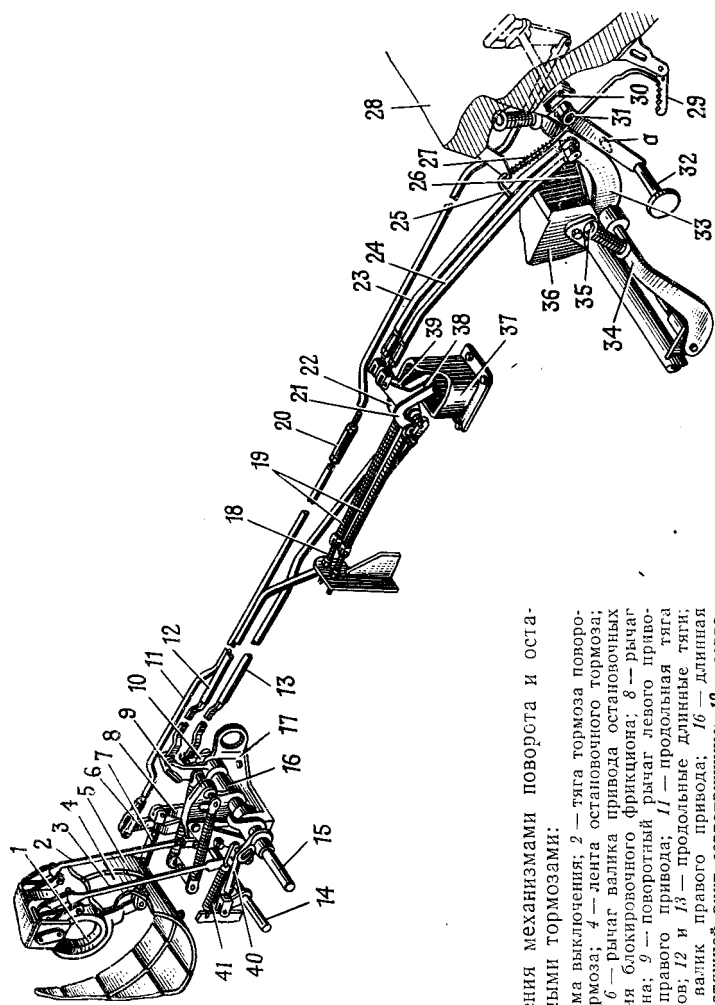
Привод управления механизмами поворота и остановочными тормозами:
